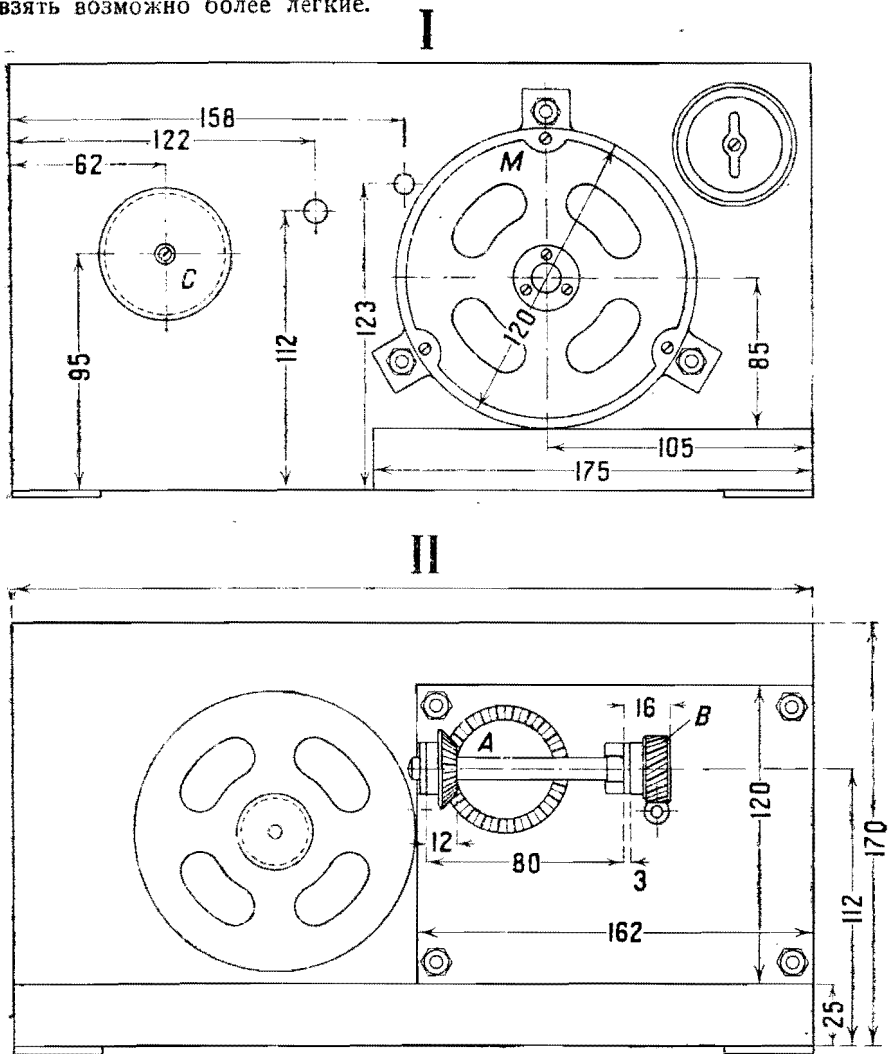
I, II. Конструкция и ориентировочные размеры лентопротяжного механизма.
